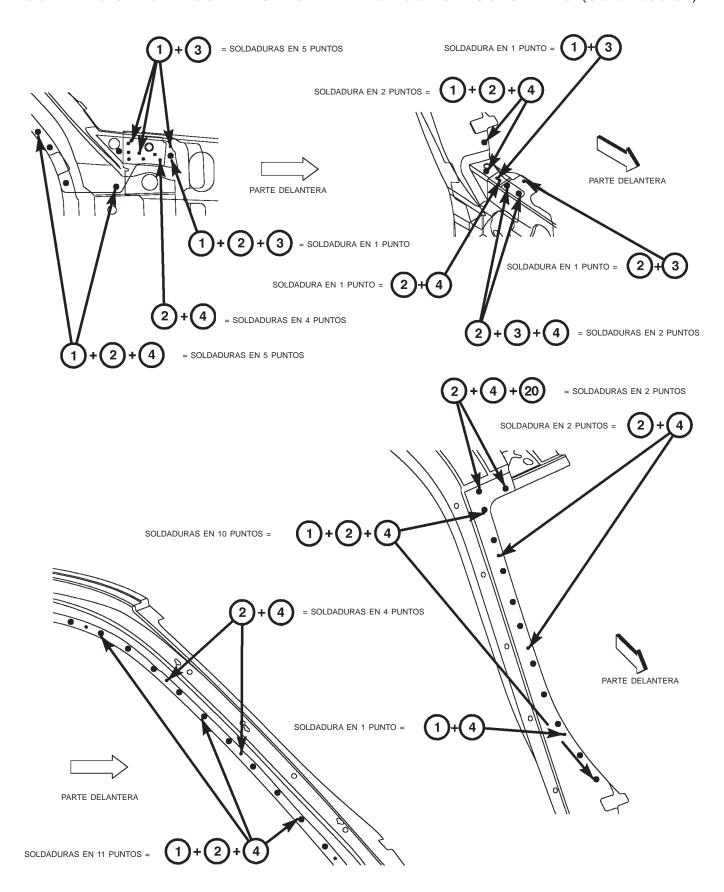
PARANTE A; REFUERZO DE GUARDABARROS
